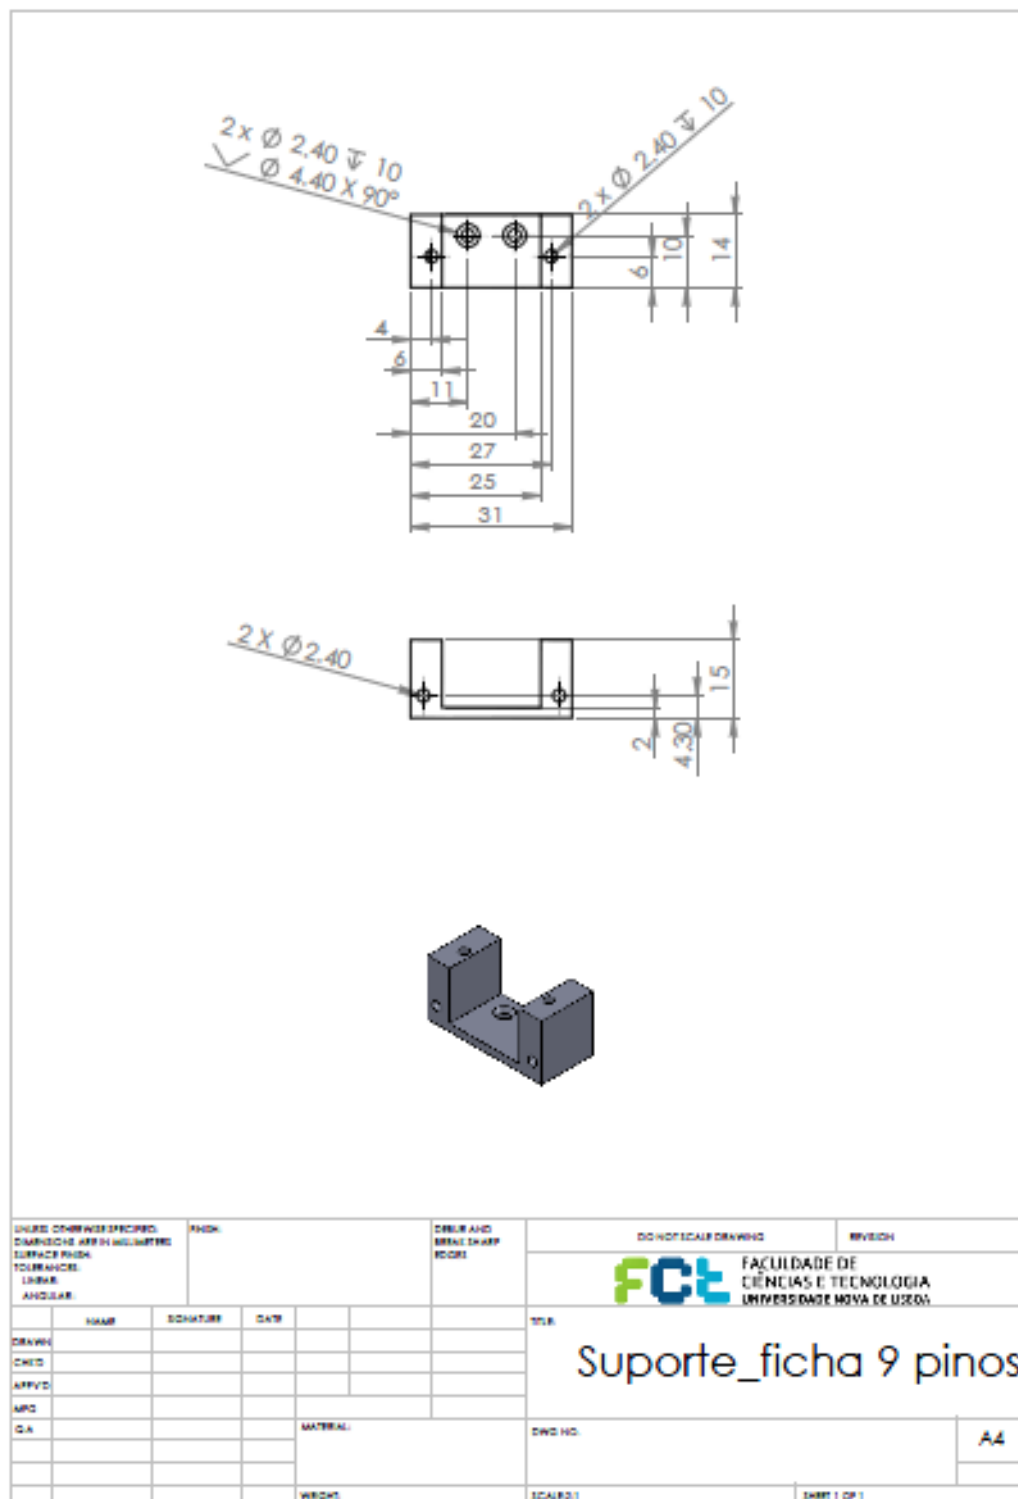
Desenho técnico do suporte da ficha de 9 pinos.
